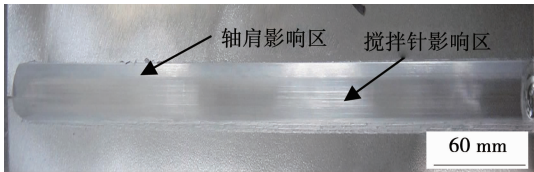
静轴肩搅拌摩擦焊 6005 铝合金接头的表面形貌
